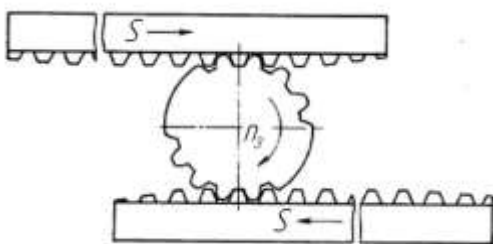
Схема накочування зубів валу плоскими рейками:  $S$  – напрям подачі;  $n_2$  – напрям обертання заготовки
